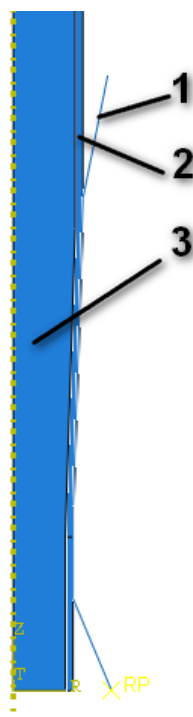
Расчетная схема конечно-элементной модели процесса волочения порошковой проволоки в металлической оболочке: 1 – проволока; 2 – металлическая оболочка; 3 – порошковый сердечник
